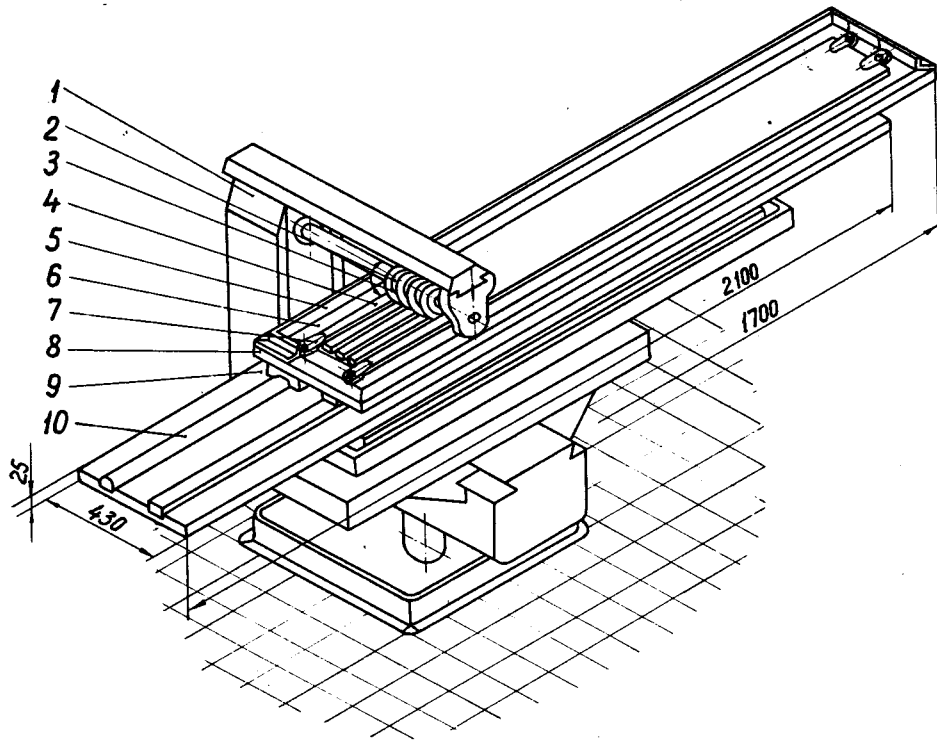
Устройство для резки стекла. 1 - станина фрезерного станка; 2 - установочные шайбы; 3 - алмазные диски; 4 - стеклозаготовка; 5 - противовес для эмульсии; 6 - подкладка из хлорвинила толщиной 3-4 мм. Подкладка предохраняет алмазные диски от вибрации при выходе их из стекла; 7 - прижимы для фиксации стекла; 8 - верхний передвижной стол с направляющими рейками; 9 - нижний стол с направляющими рейками 10, установленный на столе станка.
